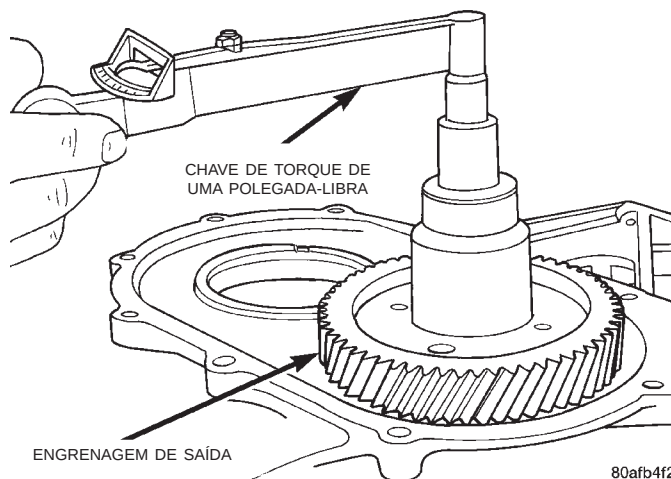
Verificação do Torque de Giro dos Rolamentos da Engrenagem de Saída
